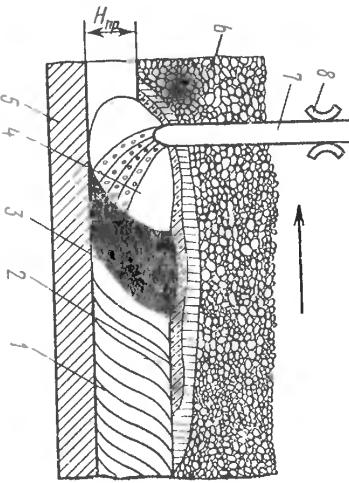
Схема дуговой сварки под флюсом:
